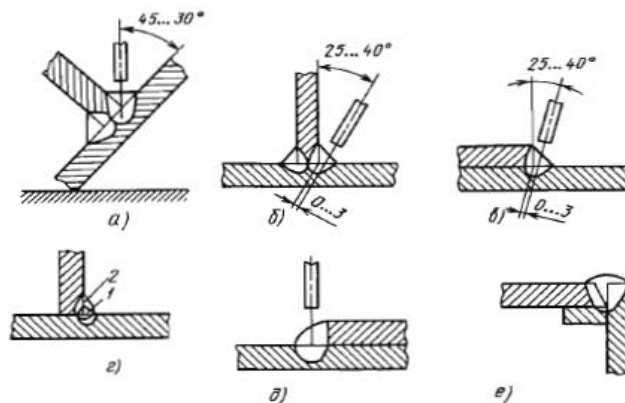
Схемы сварки угловых швов: 1 и 2 - первый и второй проходы[8].
